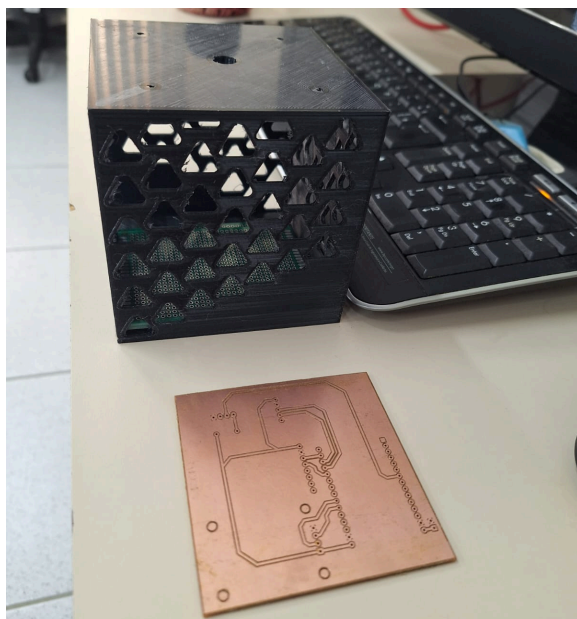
Demonstração do chassi 1U e do PCB impresso que será embarcado no CaravanaSat.
